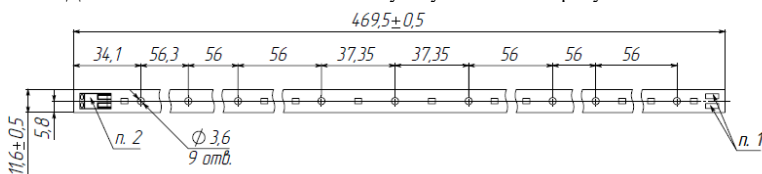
Внешний вид с габаритными и присоединительными размерами СДПП FLASH и FLASH+ TRN-Line-07W-14-2835-0702 и TRN-Line-08W-16-2835-0802 серии FLASH
